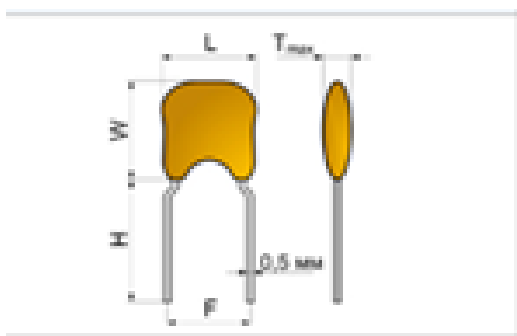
Вид корпусу конденсаторів типу К50-176
